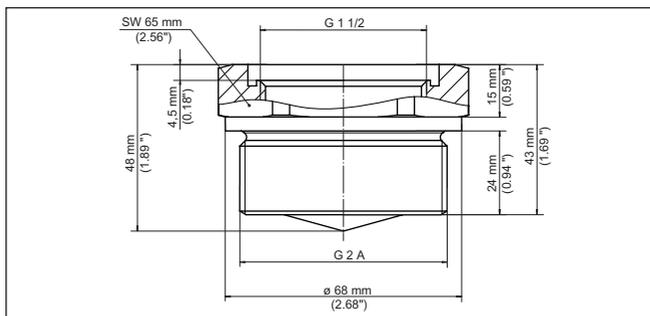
Medidas adaptador de rosca G1½ (DIN 3852-X) em rosca G2 (DIN 3852-X)
